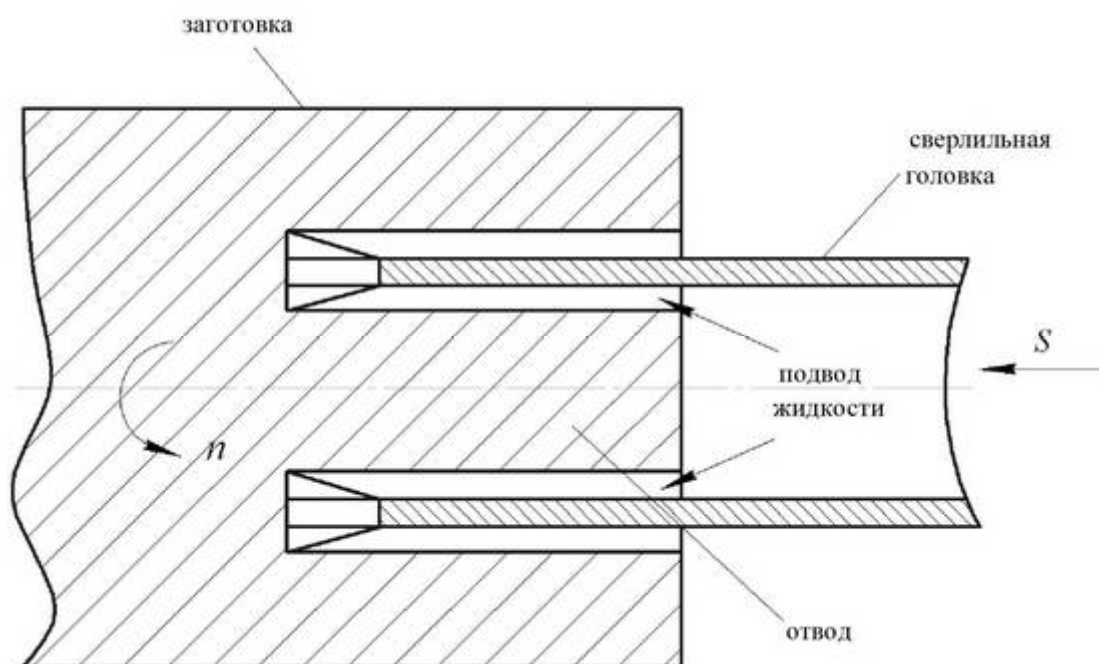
Схема высверливания центральной части заготовки в виде стержня вместо превращения ее в стружку
